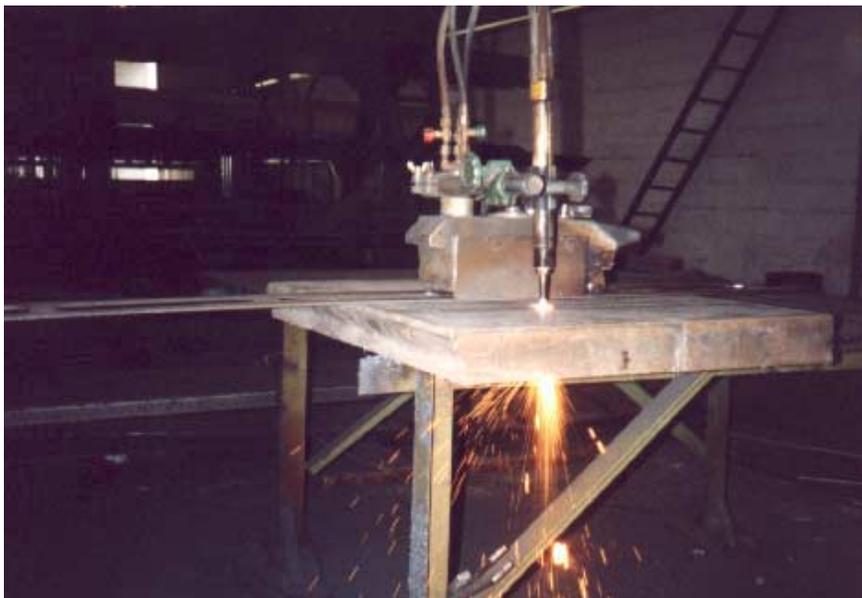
Máquina de corte térmico portátil – Tartaruga.
